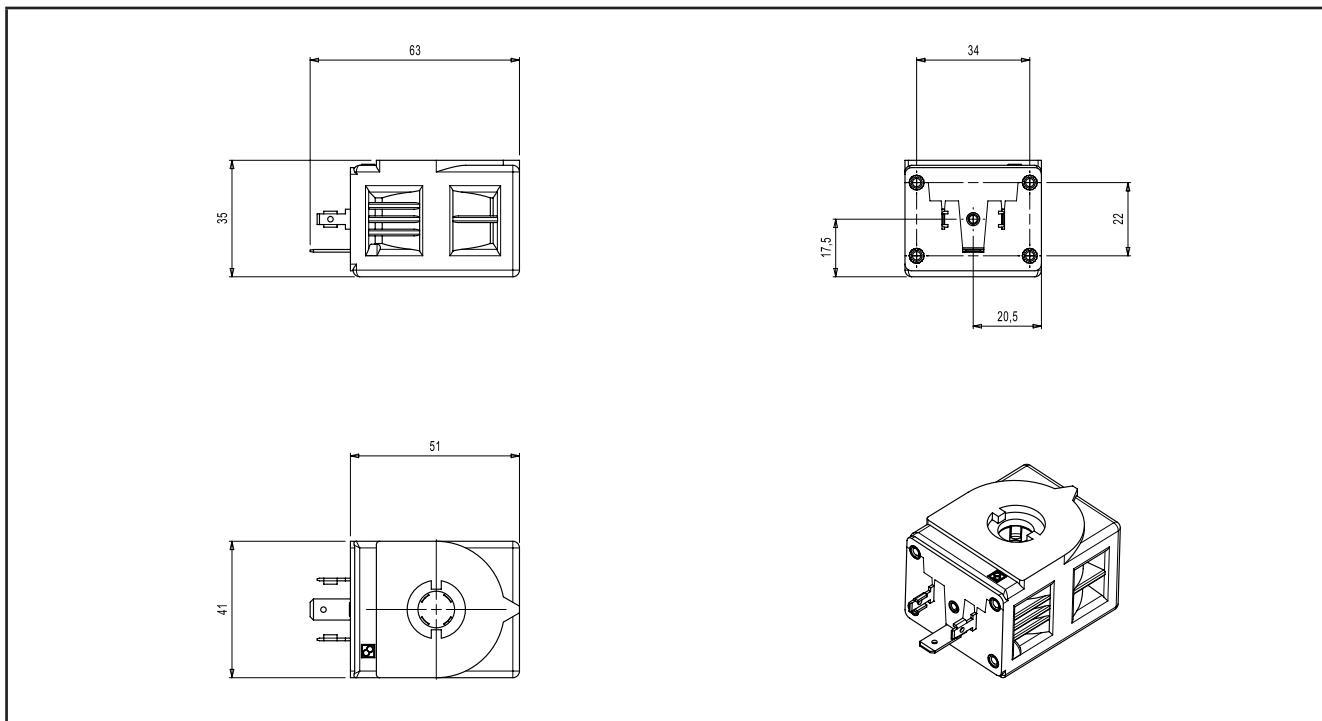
Dimensiones mecánicas bobina modelos PXVB0ARA60100, PXVB0ARA20100
